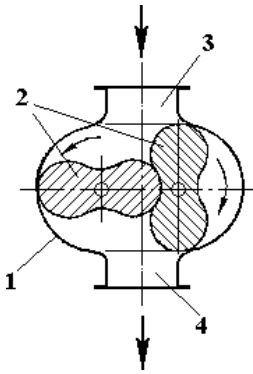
Схема ротаційної газодувки: 1 – корпус; 2 – барабан (поршень); 3 – всмоктувальний патрубок; 4 – нагнітальний патрубок
